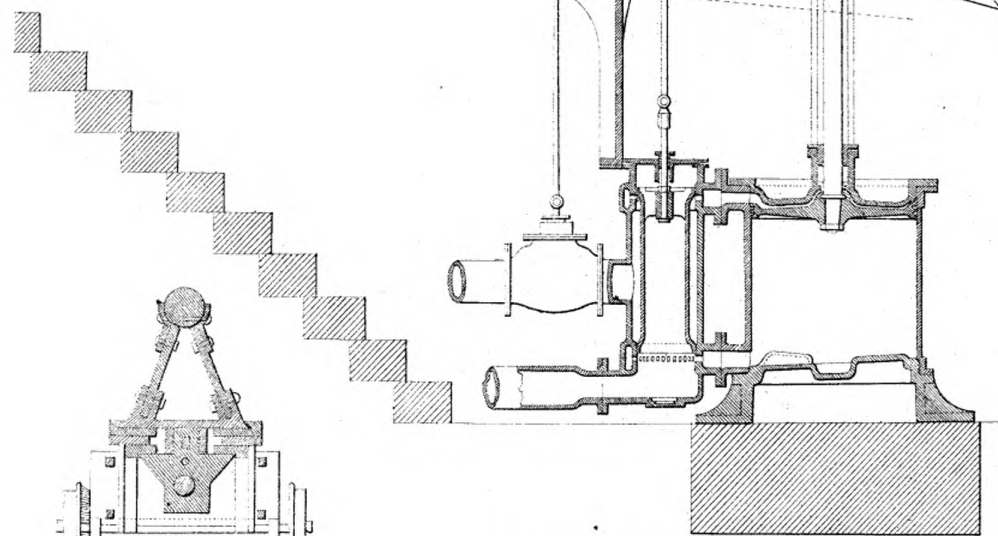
Elevation et coupe de l'ensemble du marteau d'après les dessins joints au brevet.
